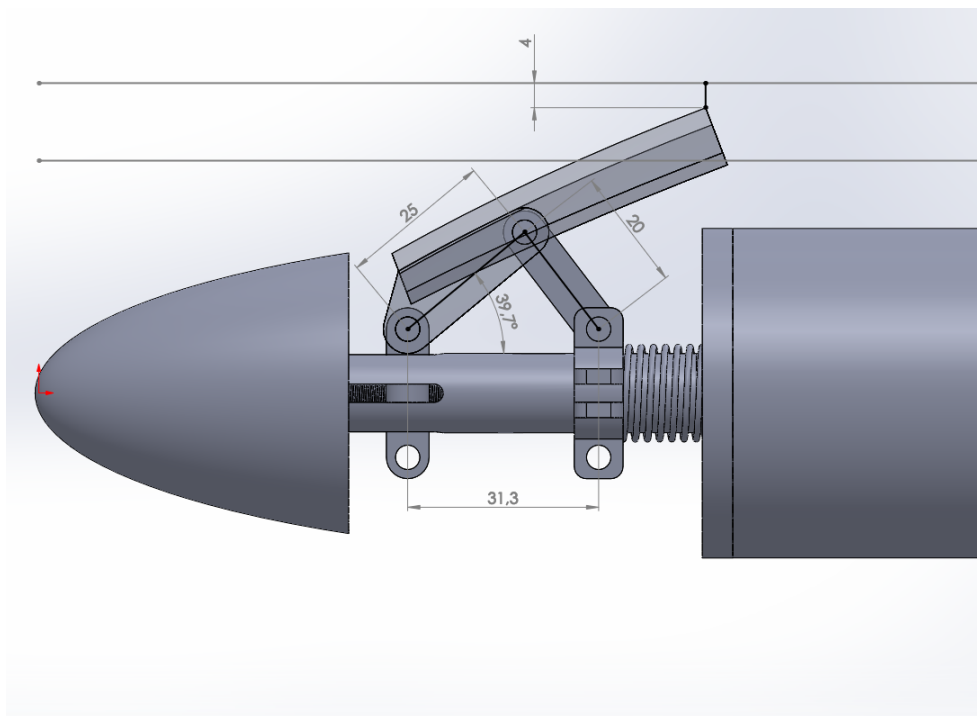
Vista de perfil com dimensões do sistema de elevação das pás para o caso de tubulação de 4 polegadas
